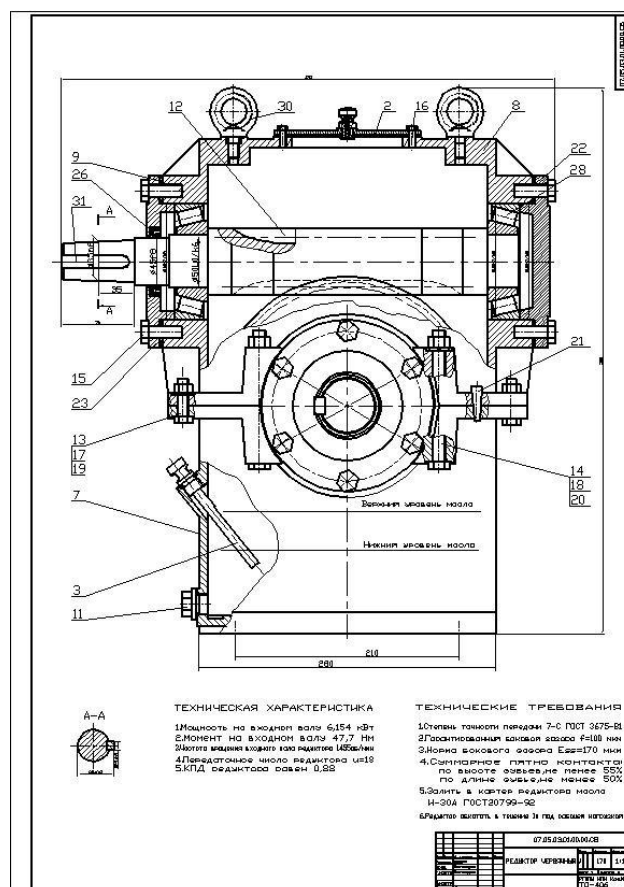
Сборочный чертеж червячного редуктора (главный вид)
